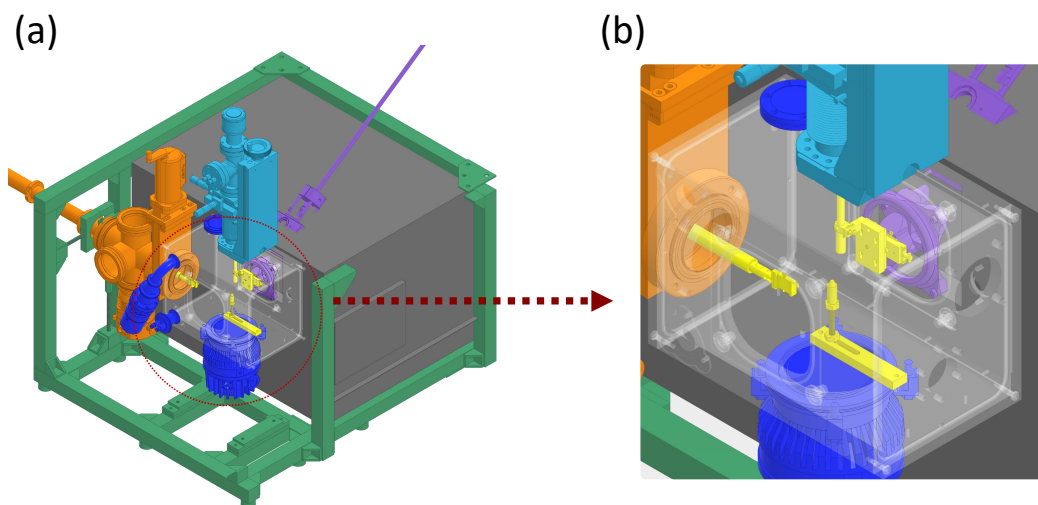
Technische Zeichnung des DINEC-MS in einer Gesamtübersicht (a) und Detailansicht der Hauptkammer (b): Zusammengehörige Baugruppen wurden in derselben Farbe markiert. Es werden die Proben-transfer- und Schleuseneinheit (orange), die Hauptkammer (weiß transparent), die Probenaufnahme (gelb), der xyz-Manipulator zur Probenpositionierung (hell blau), die Solenoid-Düse und Ionentransfereinheit (lila) und das Massenspektrometer selbst (grau) gezeigt. Zusätzlich sind die Pumpen, Messröhren, Stromdurchführungen und Schaugläser (dunkel blau) und der Aluprofil-Rahmen (grün) dargestellt.
